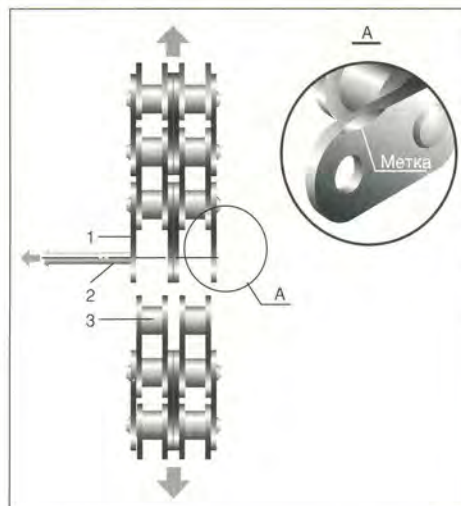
Расстыковка цепи: 1 – пластина; 2 – палец; 3 – втулка. “А” – метка (фаска).
